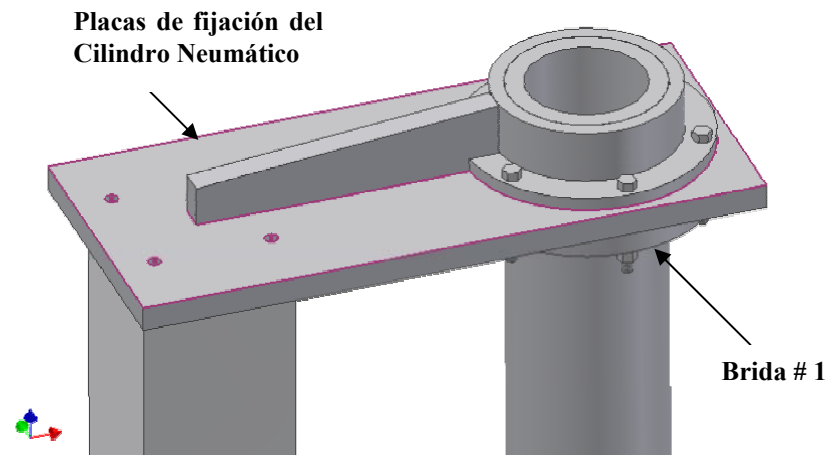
42. Vista en detalle del montaje de las Placas de Fijación del Cilindro Neumático sobre las Bridas de Agarre. Fuente: Los Autores.
